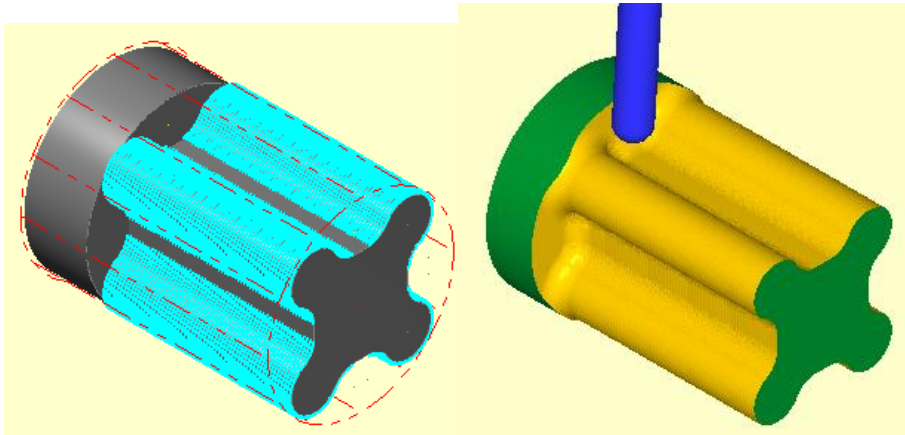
28: Tool Axis Control sekmesi Axial cut parametre şekilleri
